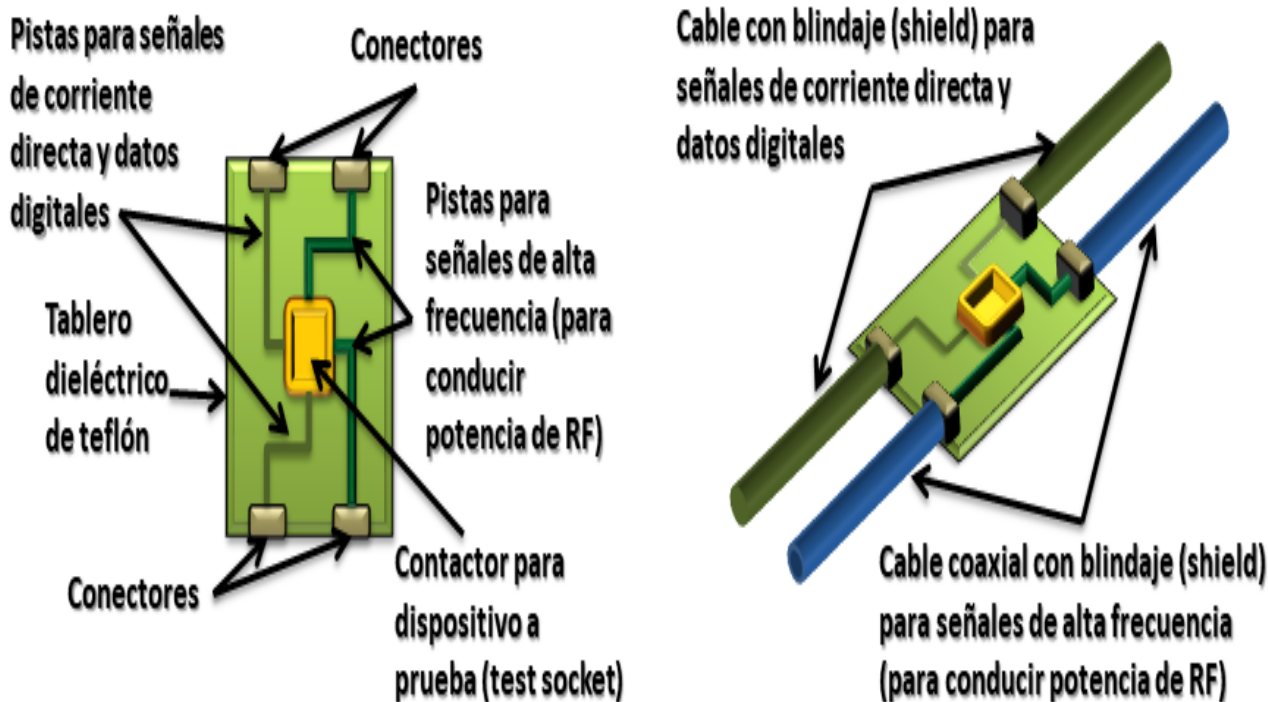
Tablero electrónico de prueba utilizado para montarse en test fixture.
